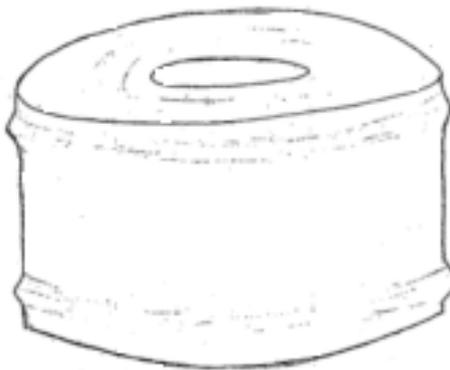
Forma de uma bobina que apresenta o defeito *build up
